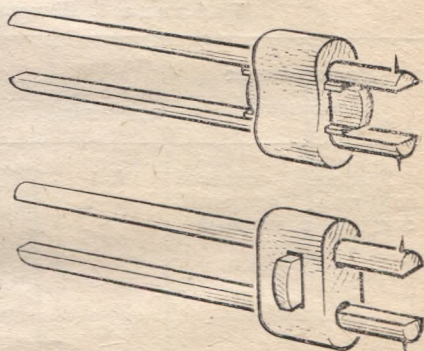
Рейсмусы с клиновым креплением брусочков.
